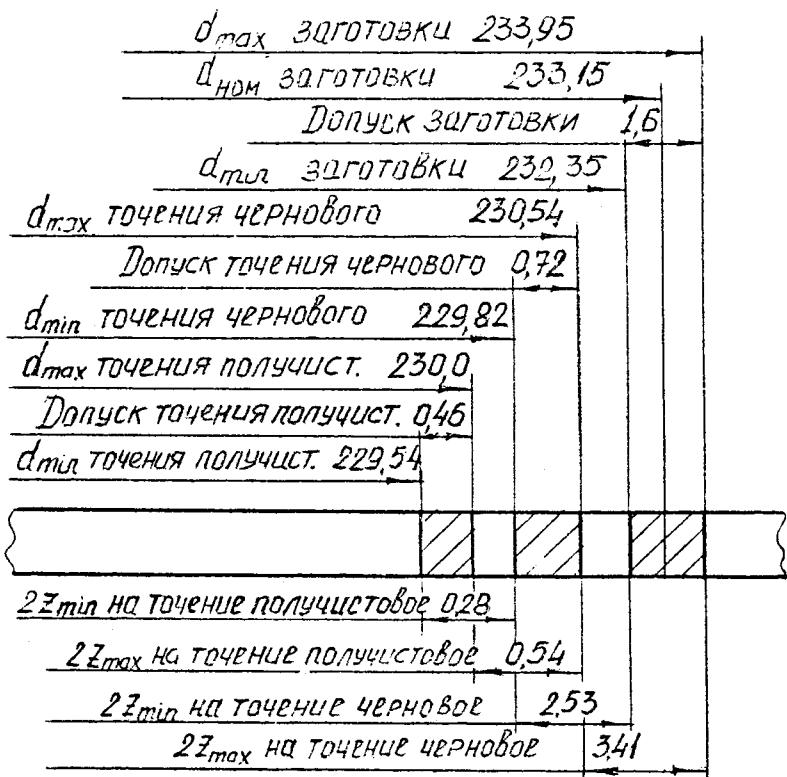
Рис. I. Схема графического расположения припусков и допусков на обработку поверхности $\text{Ø}230-0,46$ мм
